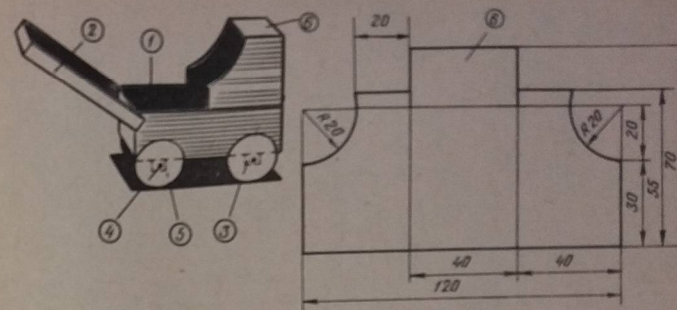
Модель детской коляски: 1—корпус; 2—ручка; 3—подшипник; 4—ось; 5—колесо; 6—тент
